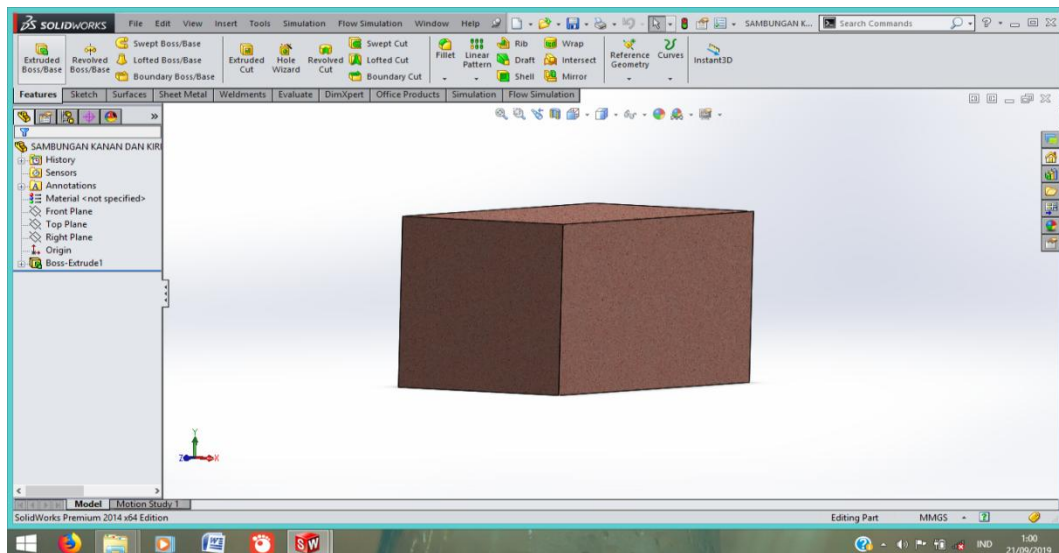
Sketch* Desain Sambungan Lantai Batu SK 34
